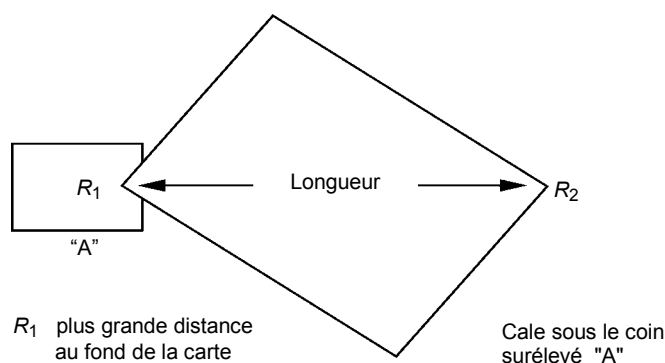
Montage de l'éprouvette pour la mesure de torsion
